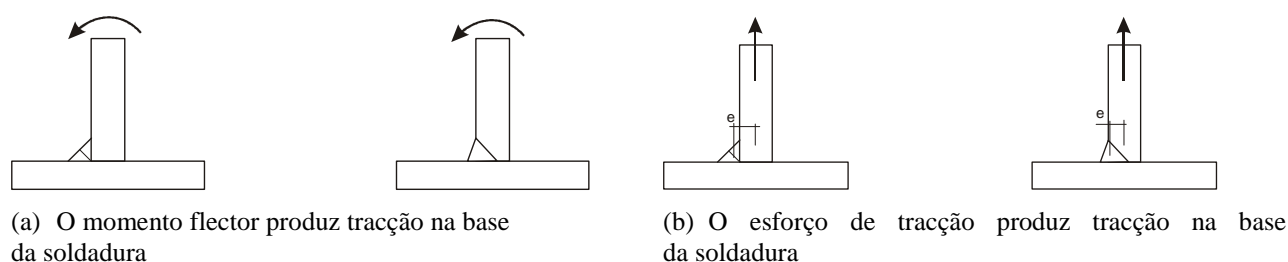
Cordões de ângulo únicos e soldaduras de topo com penetração parcial num só lado
